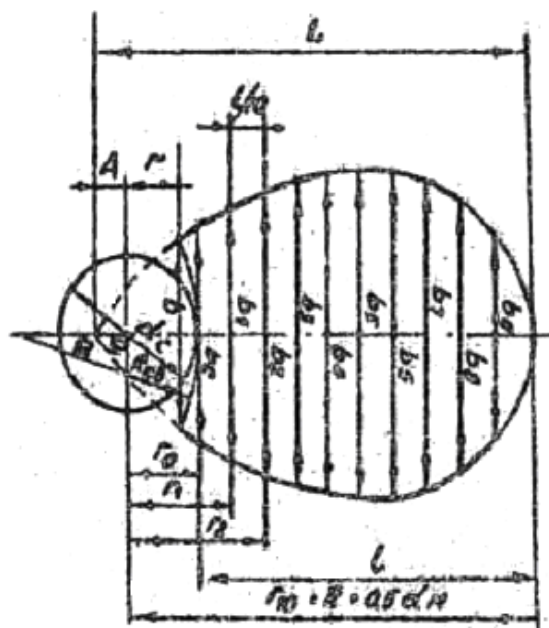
Развертка лопасти трехлопастного перемешивающего устройства
